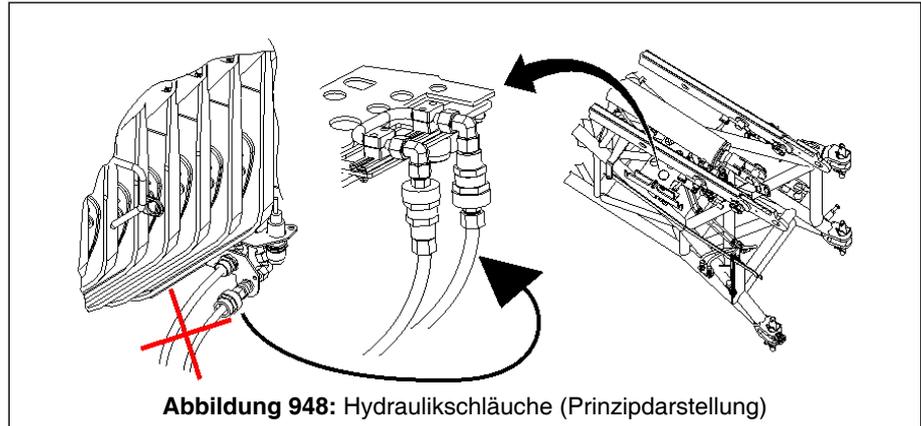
Hydraulikschläuche (Prinzipdarstellung)
